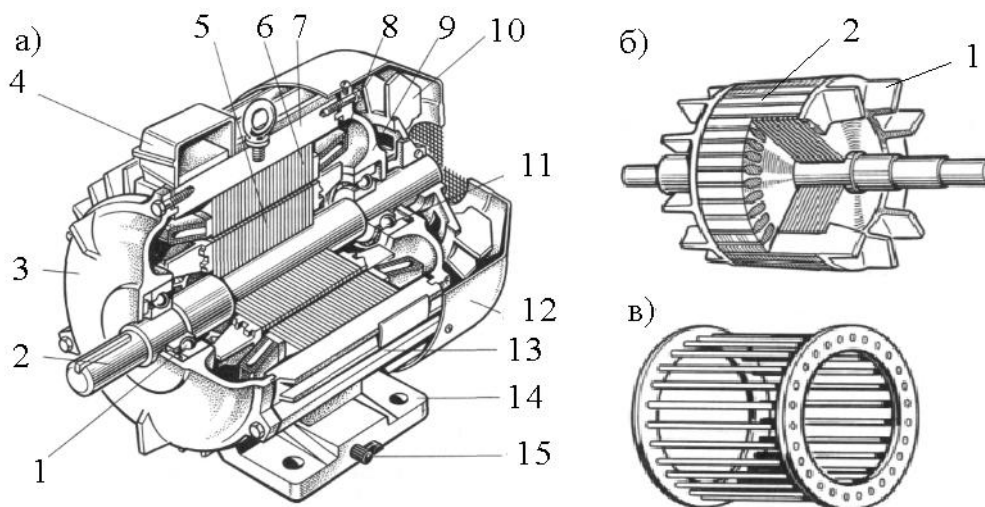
Устройство трехфазного асинхронного двигателя с короткозамкнутым ротором: а – 1, 11 - подшипники, 2 - вал, 3, 9 - подшипниковые щиты, 4 – коробка выводов, 5 - сердечник ротора с короткозамкнутой обмоткой, 6 – сердечник статора с обмоткой, 7 - корпус, 8 - обмотка статора, 10 - вентилятор, 12 - кожух вентилятора, 13 - наружная оребренная поверхность корпуса, 14 - лапы, 15 - болт заземления; б – 1- литая обмотка, 2- электротехническая сталь; в – короткозамкнутая обмотка ротора без сердечника
